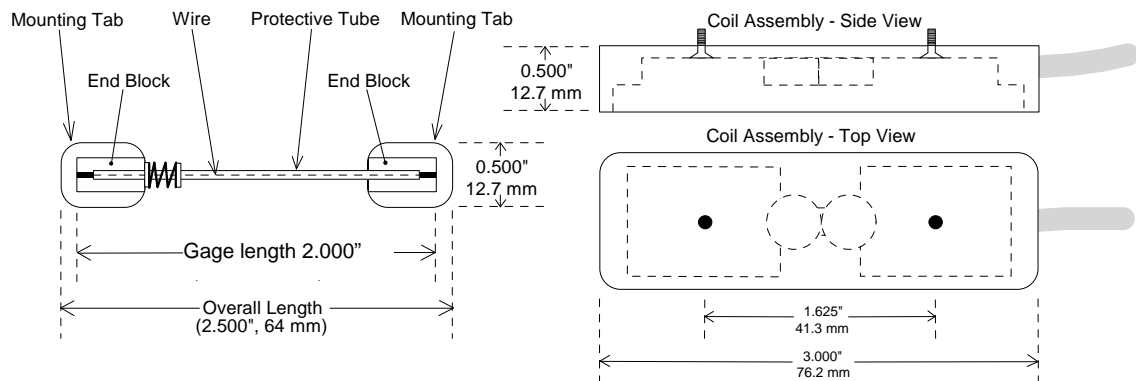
Deformímetro de Cuerda Vibrante y Montaje de Bobina
